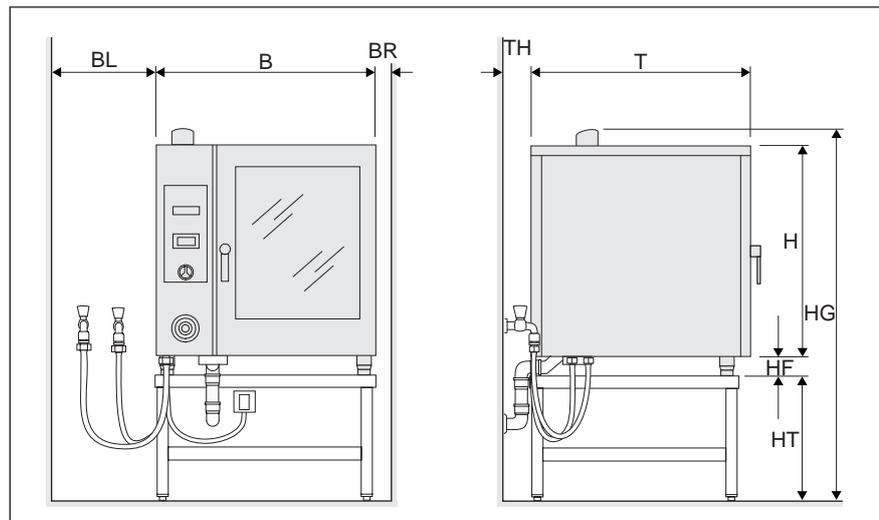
Dimensões de instalação do vaporizador combinado 615/620 e 115/120
